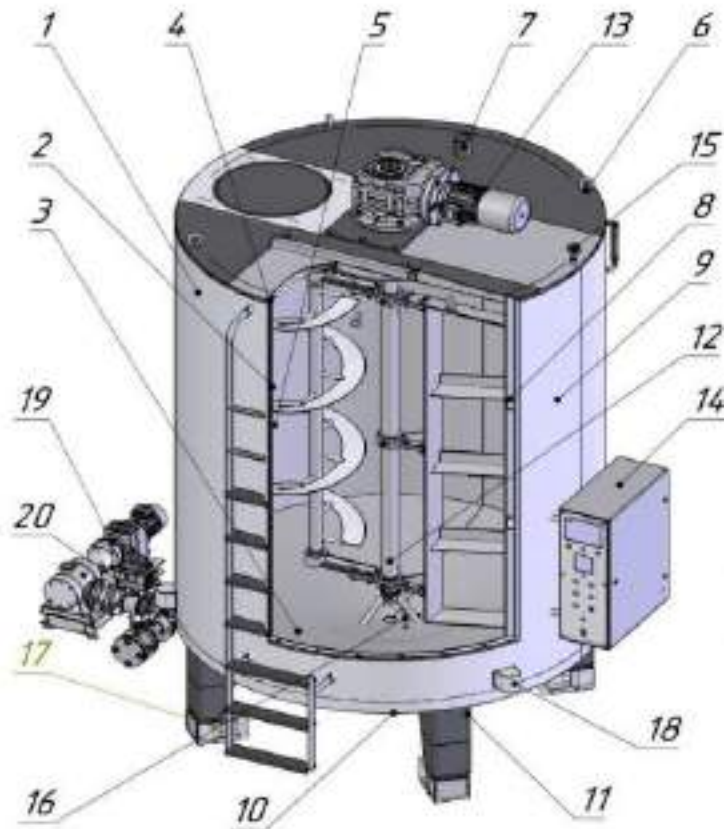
Модернізація танку-змішувачу за ексцентричною схемою розташування шнекової мішалки, де: 1 – корпус; 2 – внутрішня оболонка; 3 – внутрішній конус; 4 – фланець; 5 – змійовик; 6 – бобишка під рим-болти; 7 – патрубок загрузки; 8 – швелер; 9 – зовнішня оболонка; 10 – зовнішній корпус; 11 – опори; 12 – мішалка; 13 – привід; 14 - шкап управління; 15 – датчик оболонки; 16 – датчик продукту; 17 – тензометр; 18 – тени; 19 – насос вивантаження продукту; 20 – патрубок вивантаження продукту
